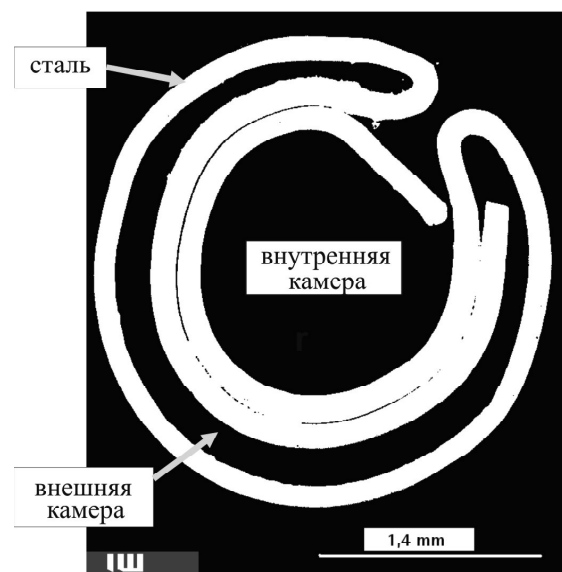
Сечение двухслойной порошковой проволоки [5]
